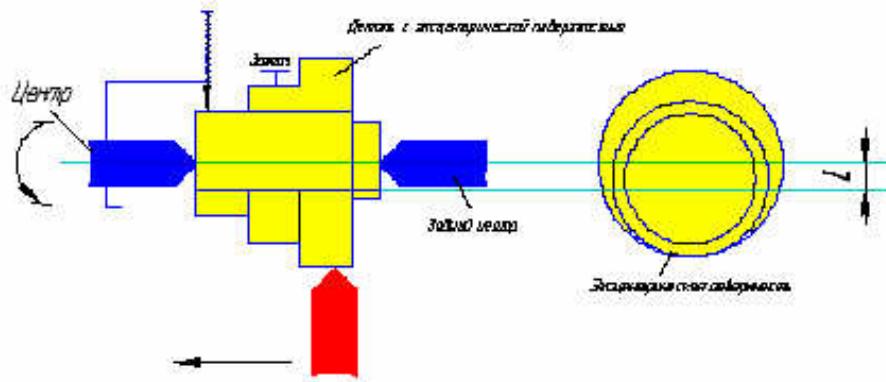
Обработка деталей на эксцентрично установленной оправке
